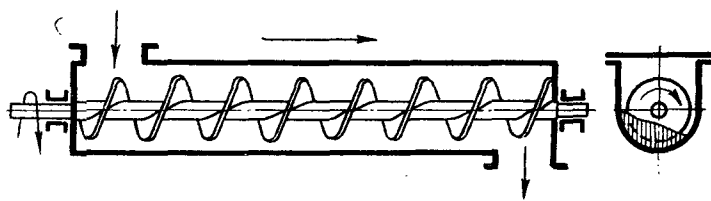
Винтовой транспортер или шнек для свинцового порошка
